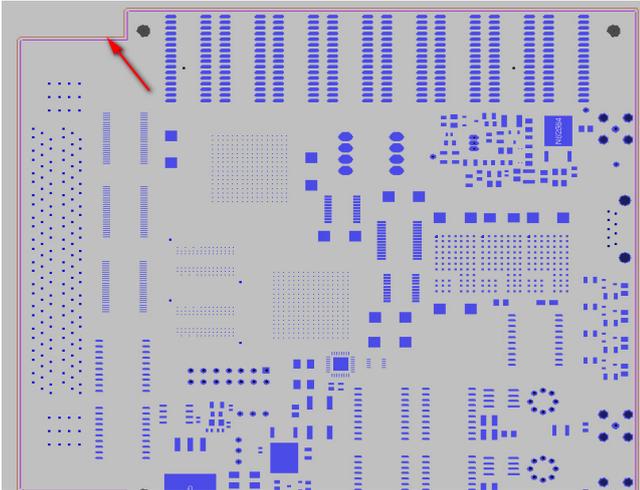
Контур платы в OrCAD PCB Designer
